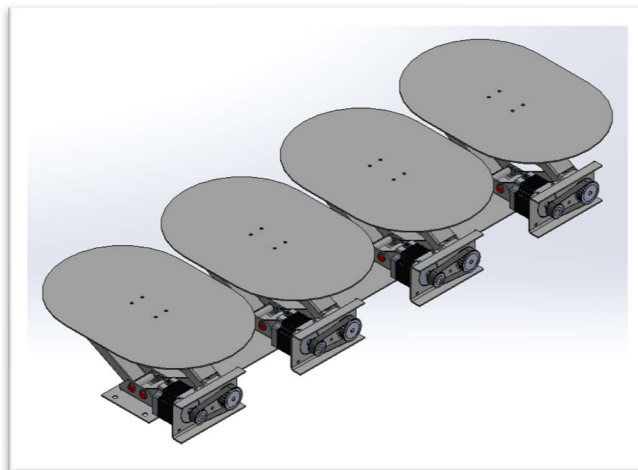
Módulo elevadores x4. Fuente: Elaboración propia
